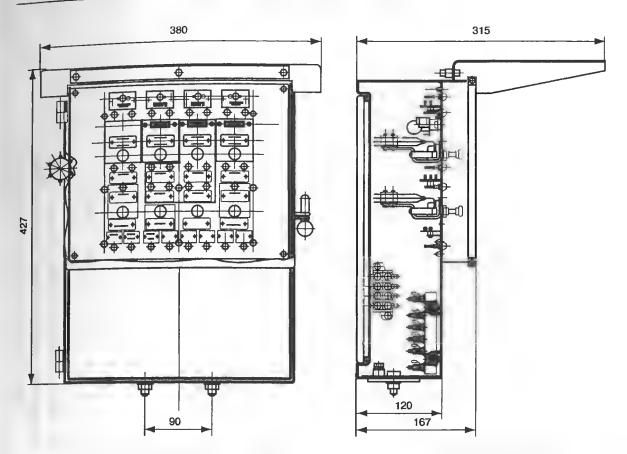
Габаритные и установочные размеры щитка ЩПС-2000
